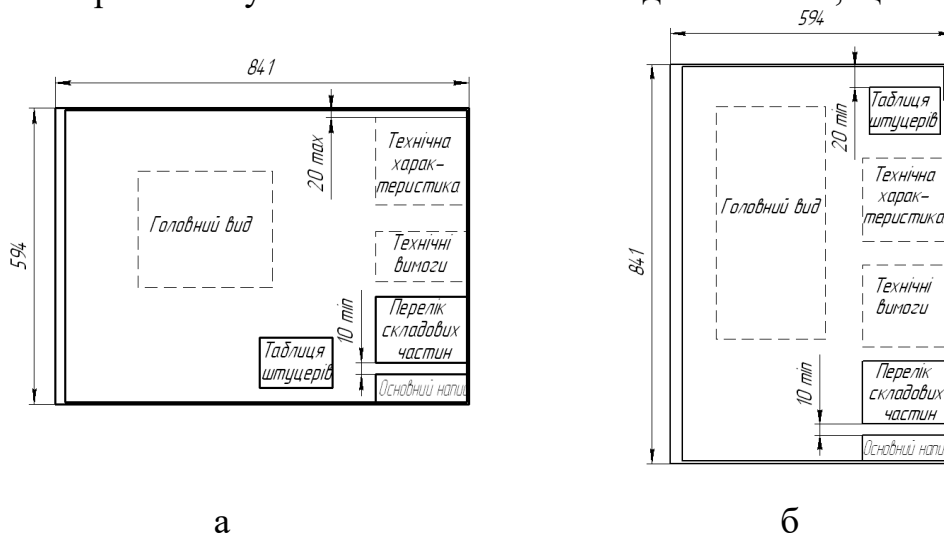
Зразок розташування елементів кресленника загального виду [1]:
